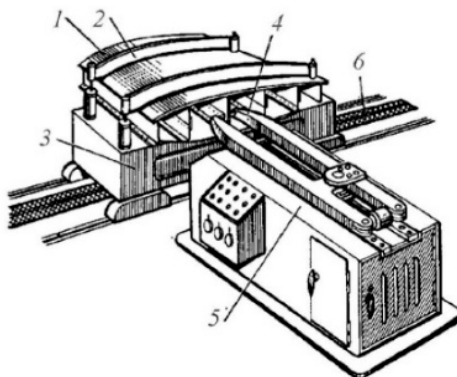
Автоматизированная установка для точечной сварки
